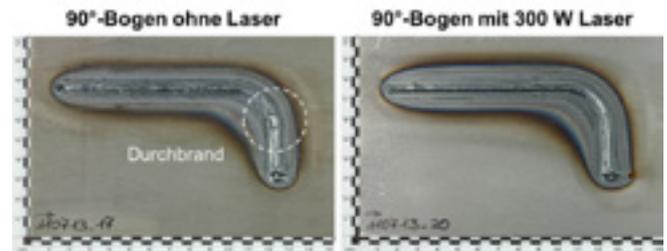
Oberraupe eines plasma- bzw. hybrid-geschweißten 90°-Nahtbogens mit konstant 100 cm/min Vorschubgeschwindigkeit bei 2 mm Blechdicke.
